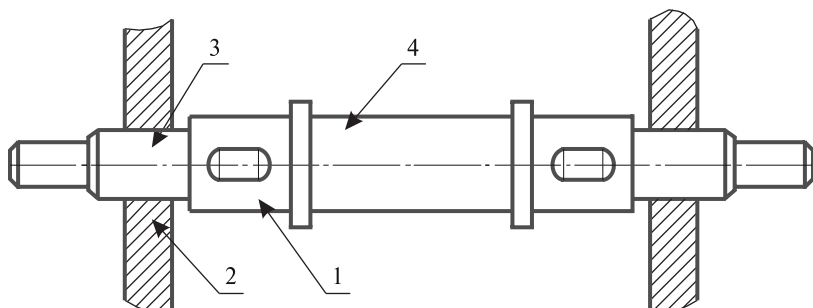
Прямой вал: 1 – вал; 2 – опоры вала; 3 – цапфы; 4 – шейка
